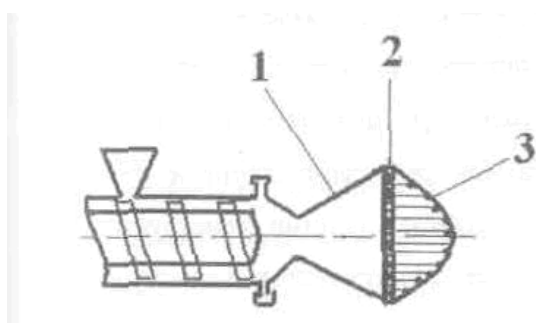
Схема формования БП с использованием пресс-инструмента с матричной обоймой [54]:
